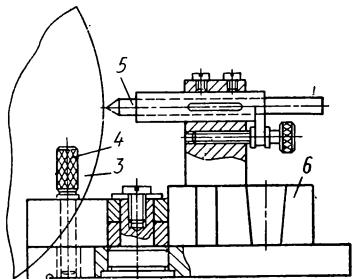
Приспособление для ручной правки круга на профилешлифовальных станках:
